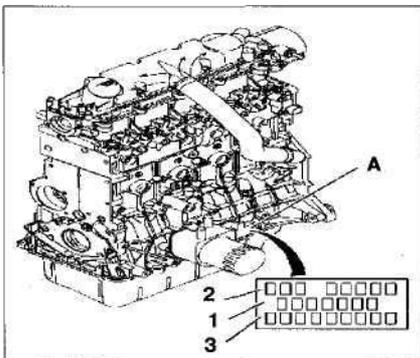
Маркировка А, в которой указаны: метка узла 1, разрешенный тип 2 и заводской порядковый номер 3.
